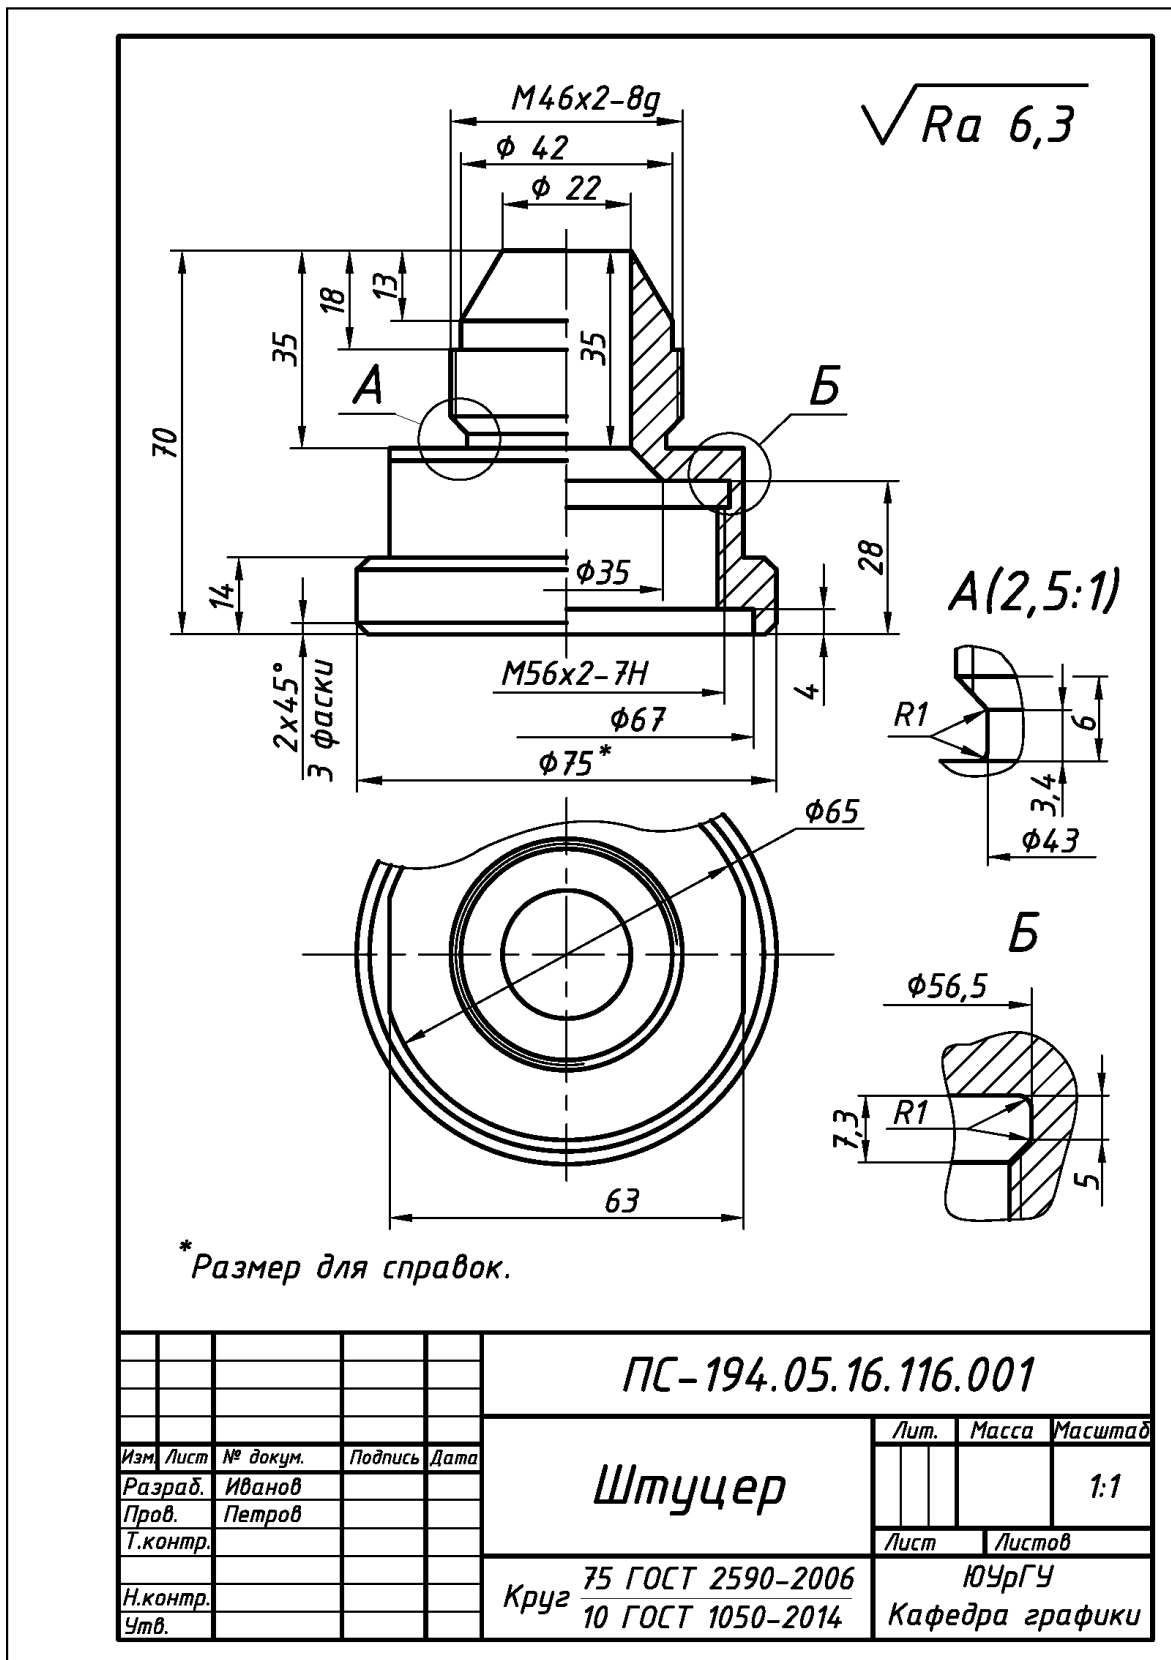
Пример выполнения и оформления рабочего чертежа детали «Штуцер» (поз. 1), входящей в состав чертежа сборочного изделия «Клапан воздушный» (см. рис. 8.3)
